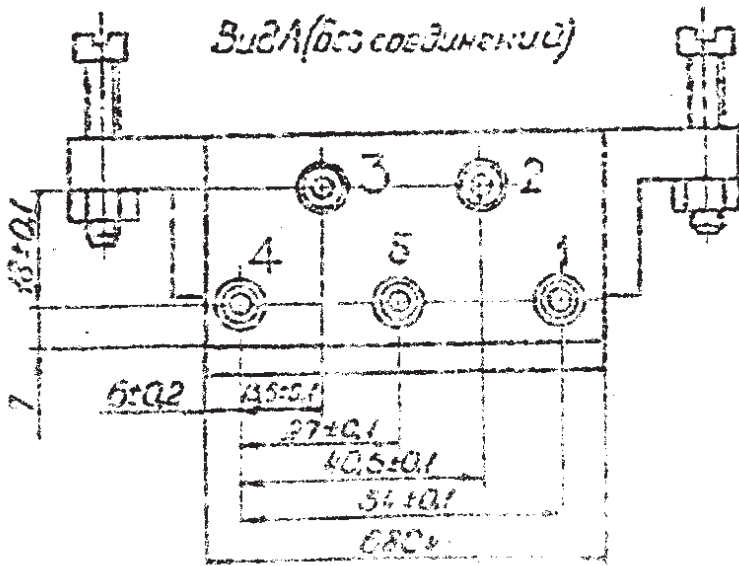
Габаритные, установочные и присоединительные размеры регулятора ПРЭ.34-М1
